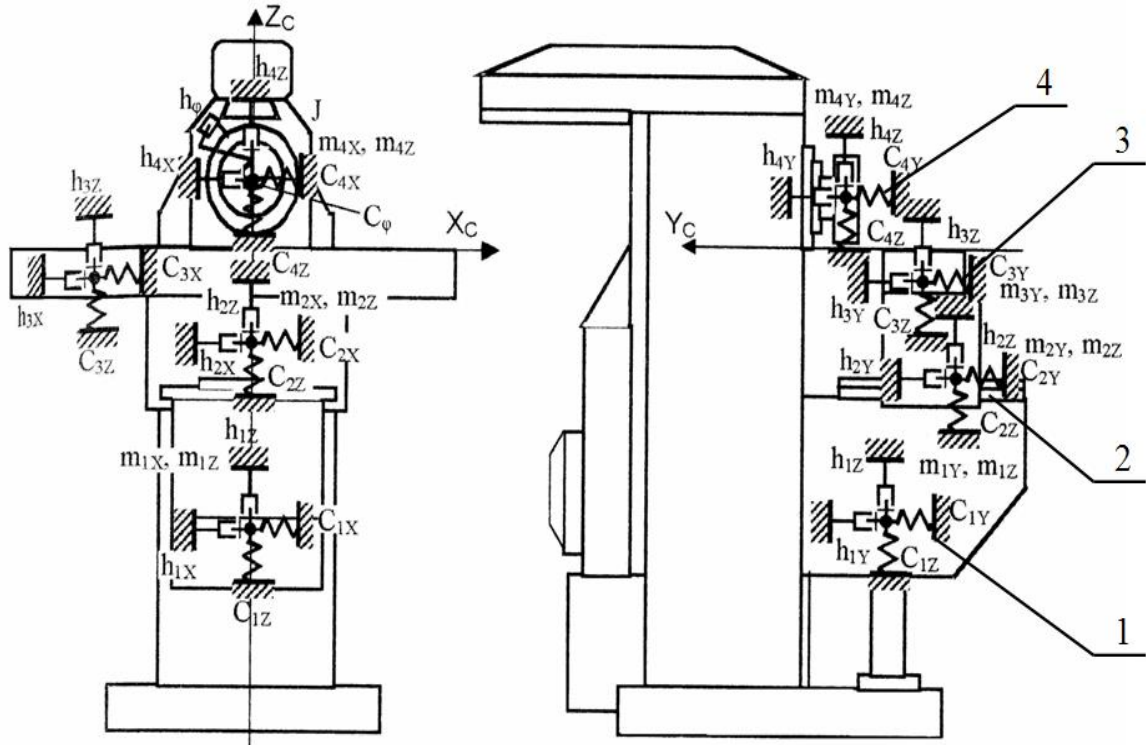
Схематизация исполнительного механизма фрезерного станка
